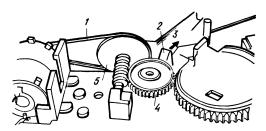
Снятие двигателя привода тонарма: I — пассик. 2 — стопор, 3 — нажать стопор в направлении, указанном стрелкои, 4 — промежуточное зубчатое колесо, 5 — червяк
